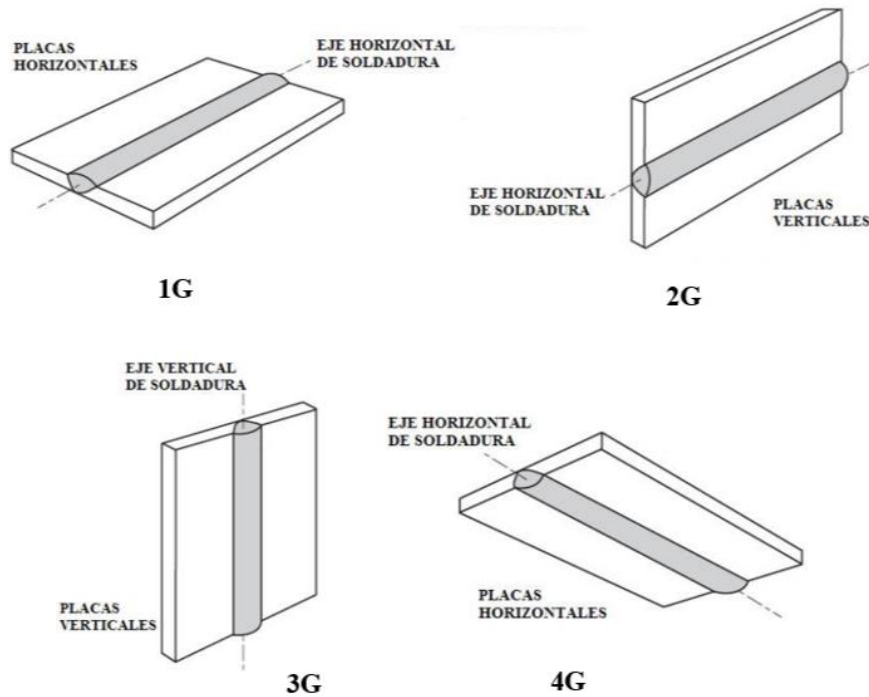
Posiciones de soldadura para ranuras. [15]
